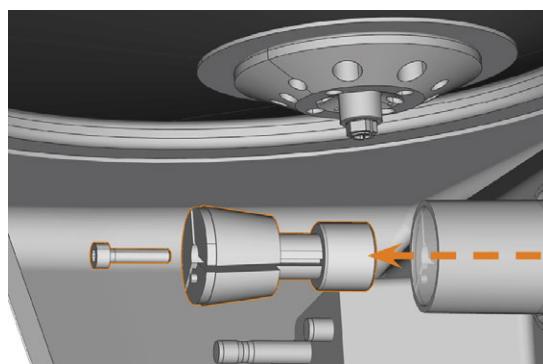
RIMOZIONE DELLA PINZA DI SERRAGGIO DAL PORTAPEZZI
